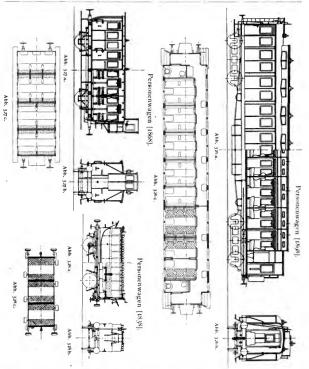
d. Grundriss eines Personenwagens.
